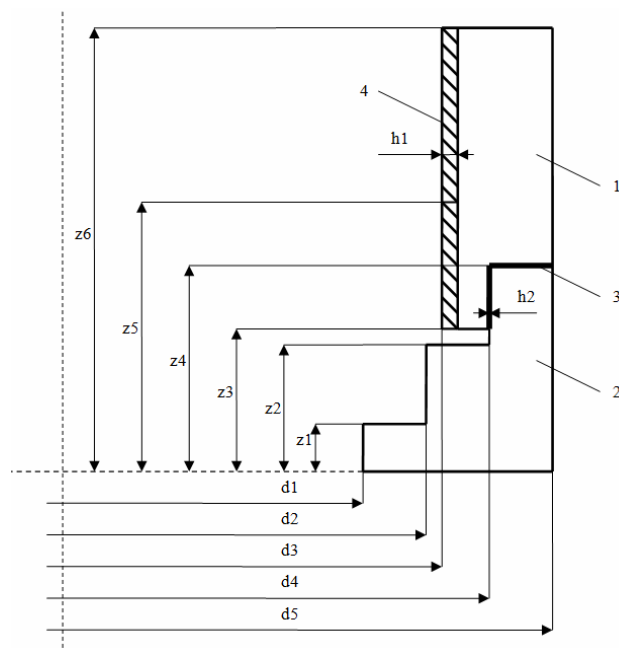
Схема поперечного сечения паяного корпуса гидроцилиндра
